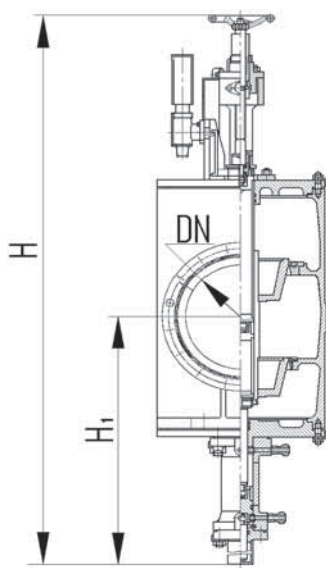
Клапан регулирующий проходной фланцевый с гидроприводом
